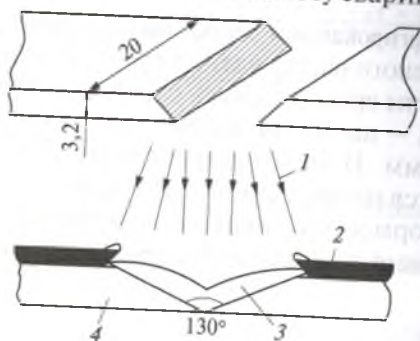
Схема процесса сварки КМ напылением:
